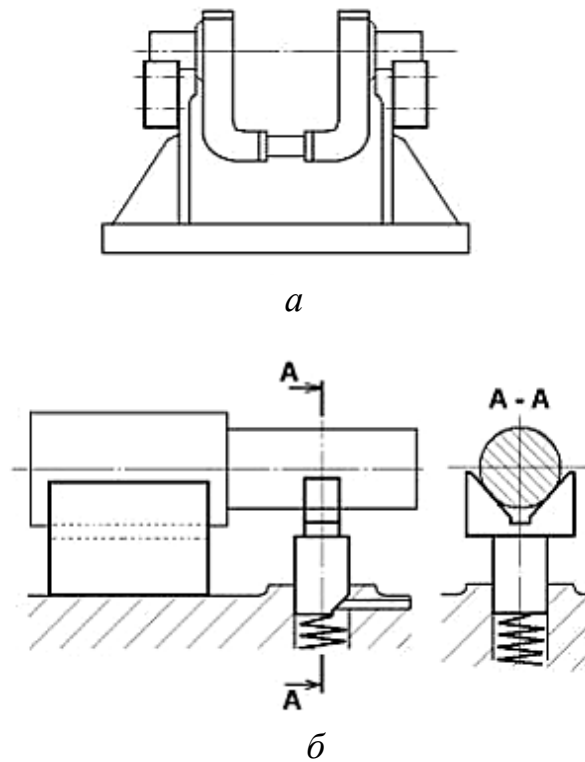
Примеры установки заготовок наружной цилиндрической поверхностью:
